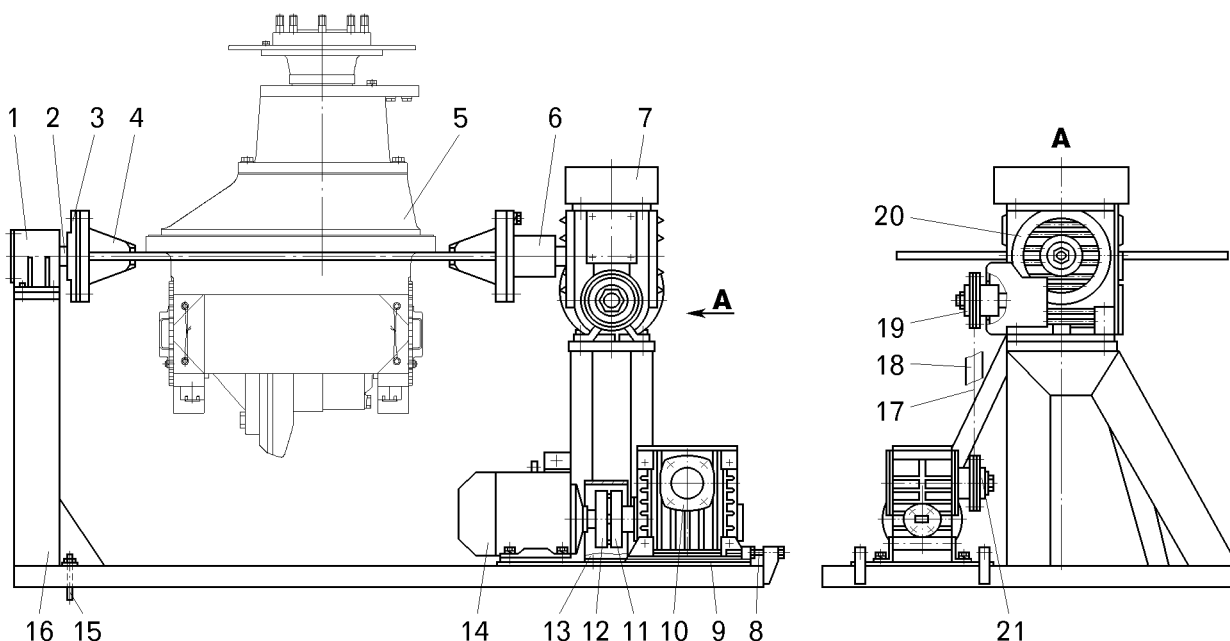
Стенд-кантователь для сборки и разборки главной передачи ведущего моста:
